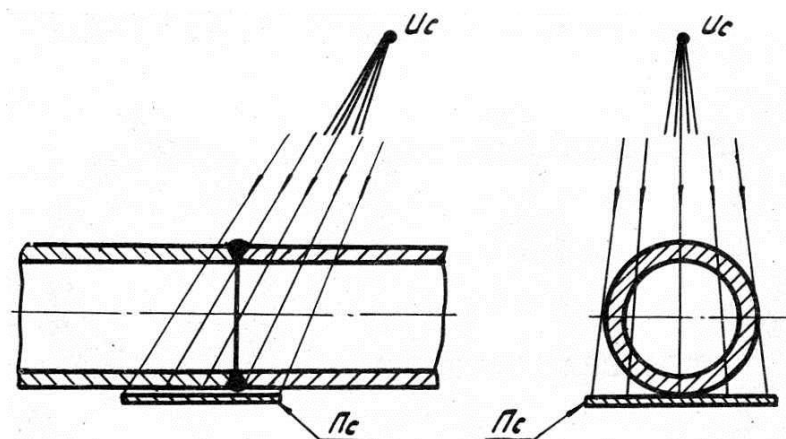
Схема фронтального просвечивания кольцевого сварного шва через две стенки на плоскую кассету за две установки источника излучения (схема просвечивания «на эллипс»)
